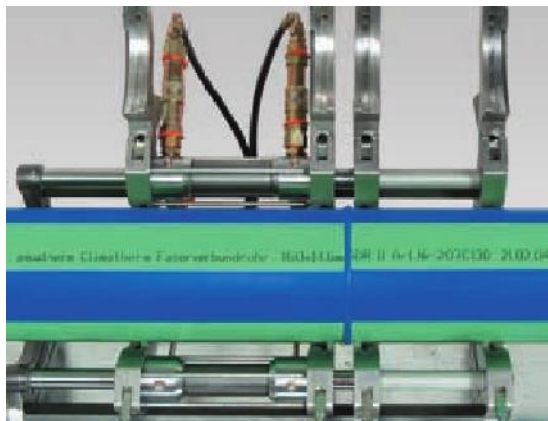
Soldadura topo a topo de tubos de polipropileno [51]
